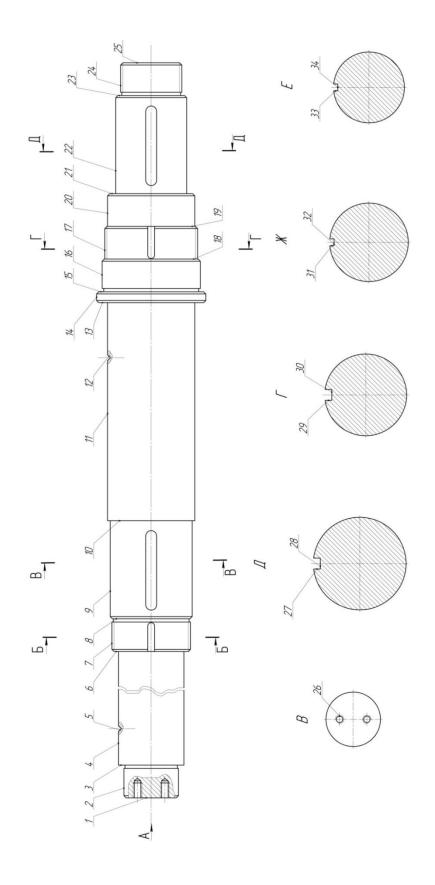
Общий вид детали - «Вал тихоходный»
